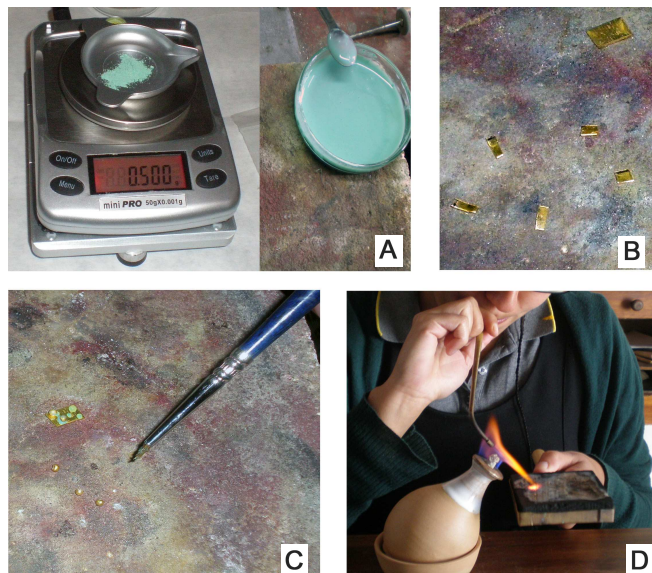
Proceso de soldadura por sal de cobre. A) Producción de la solución por sal de Cu, B) producción de los gránulos, C) posicionamiento de los gránulos con la solución de sal de Cu sobre la lámina, D) soldadura de los gránulos a la lámina mediante el uso de un soplete.
